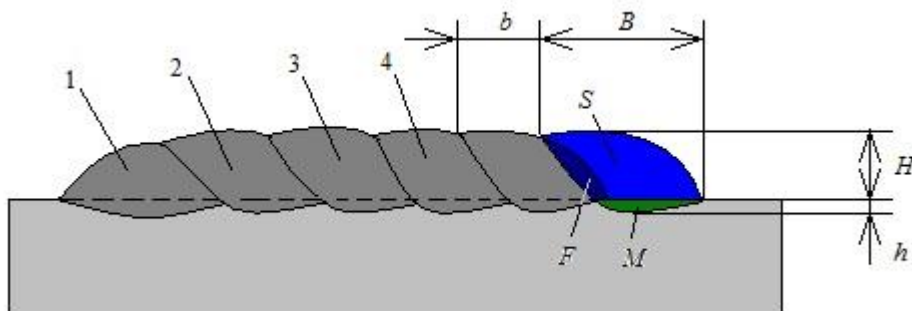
Поперечное сечение последовательно наплавляемых валиков в один слой: 1...4 – номера валиков; b – смещение дуги; B – ширина наплавочной ванны; S , F , M – сечения наплавки, переplava предшествующего валика и расплава подложки; H – высота наплавки; h – проплавление подложки
